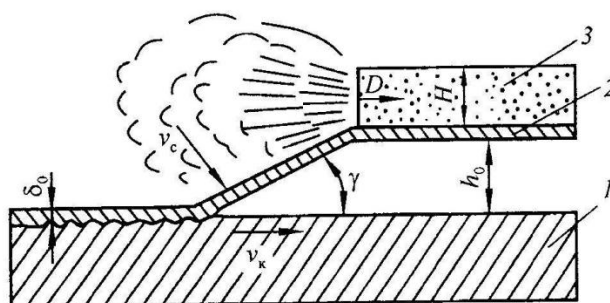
Схема сварки взрывом плоских двухслойных заготовок
